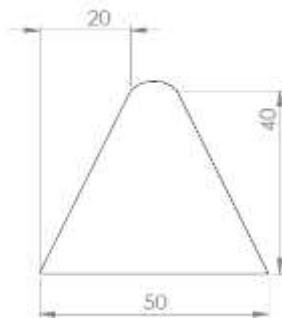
Plano de pieza a fresar mediante función G08. Fuente (El autor).
